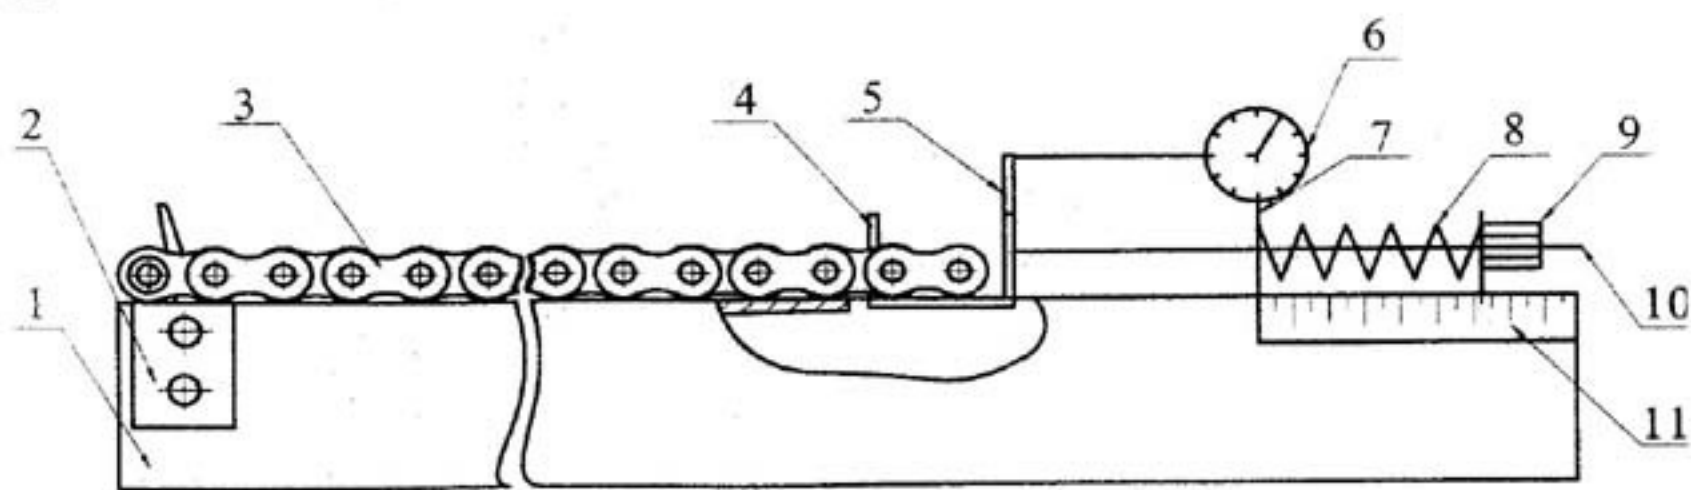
Схема приспособления для измерения удлинения цепи с винтовым нагружением
